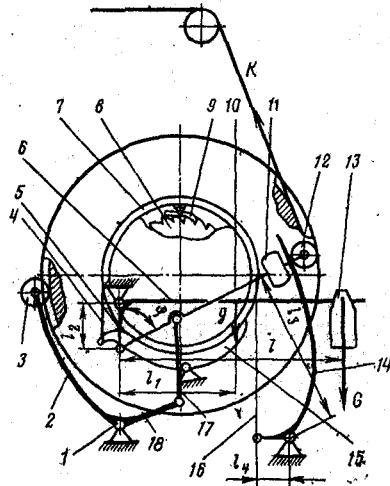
Схема автоматического основного тормоза станка АТ-175
